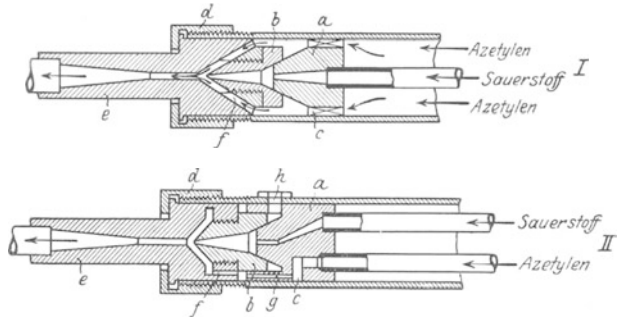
Schweißbrenner mit Sauerstoffrücktrittsicherung.
